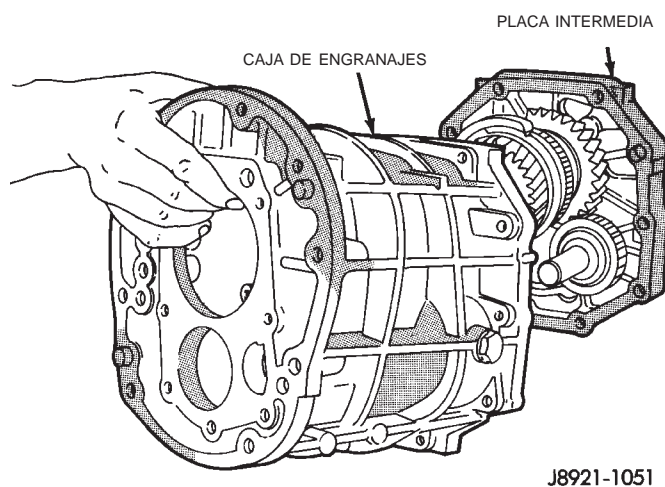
Desmontaje de placa intermedia de la caja de la transmisión
